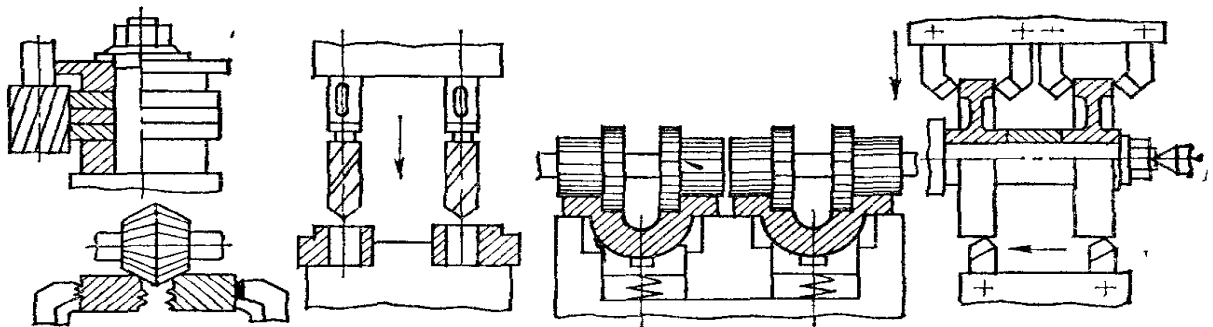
Схеми багатомісної паралельної багатоінструментної обробки з одночасним встановленням заготовок
